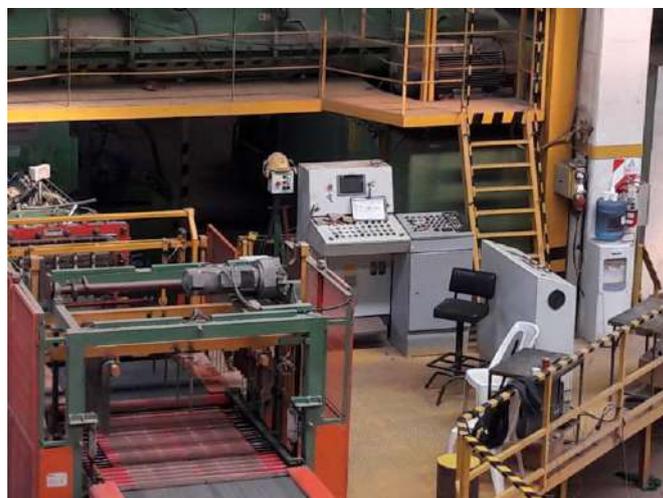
"Puesto de trabajo del extrusorista" - Fuente: Propia
